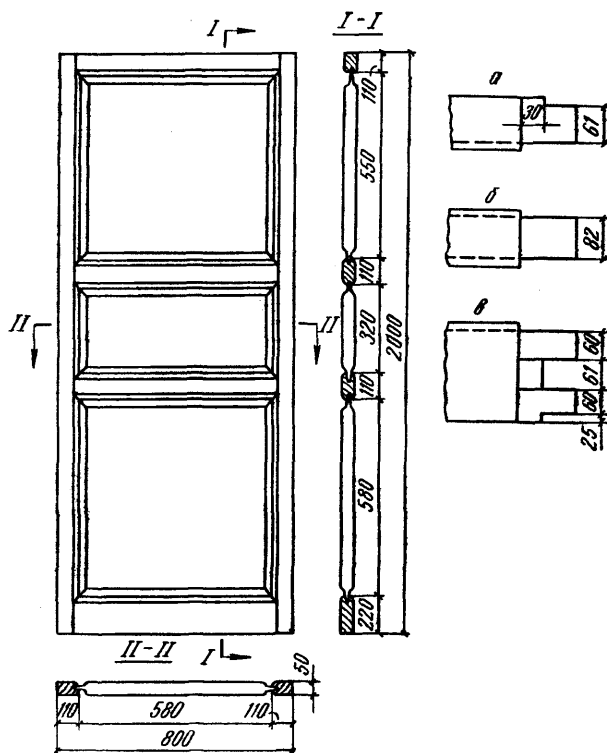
Рабочий чертеж дверного филенчатого полотна:
